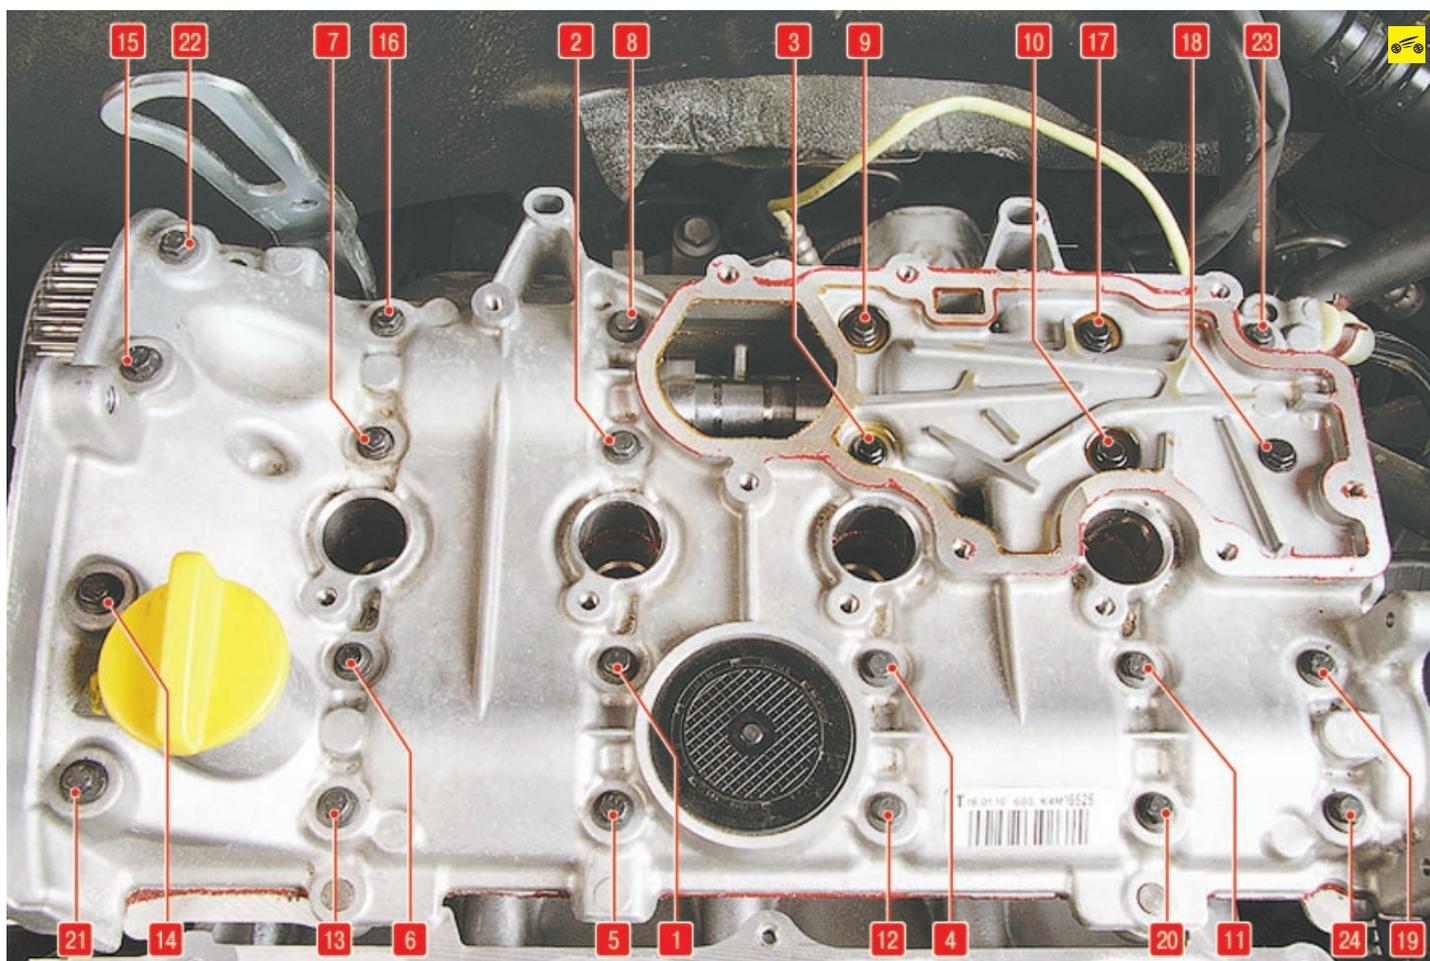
Порядок затяжки болтов крепления крышки головки блока цилиндров
